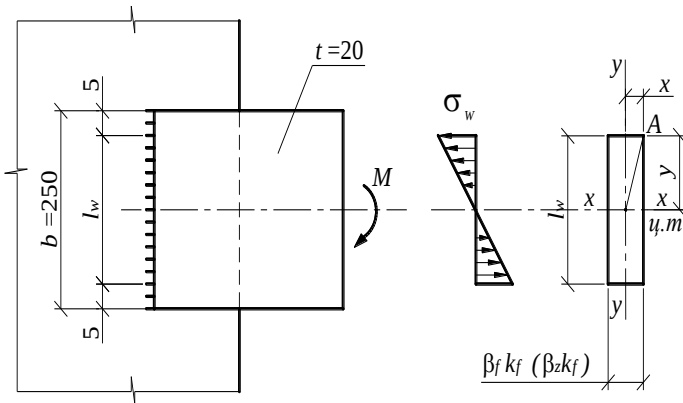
К расчету сварного соединения на чистый изгиб
